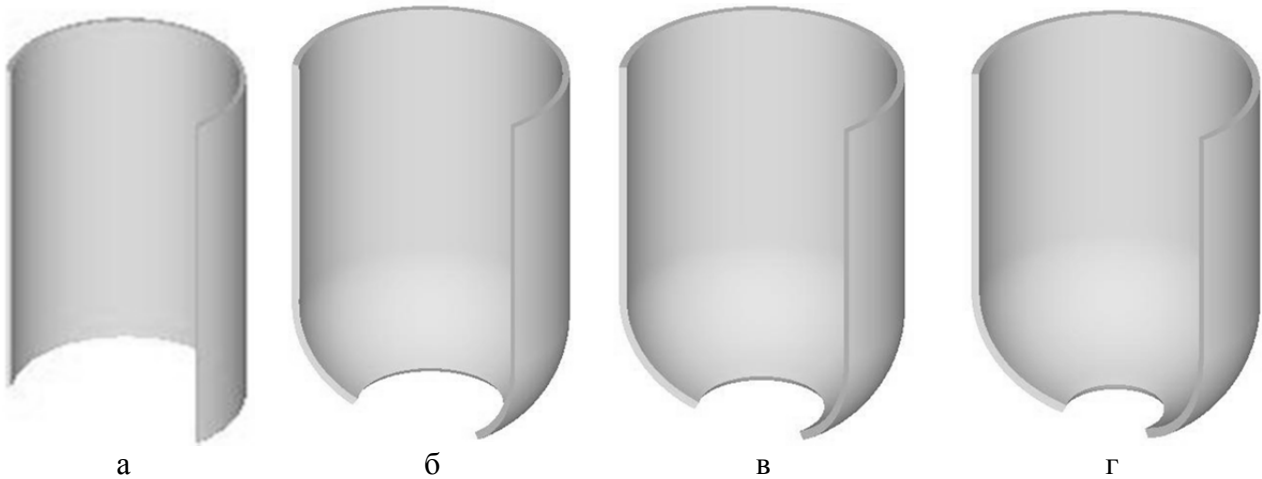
Вихідна заготовка в розрізі (а) та здеформовані заготовки з протитиском $q = 0$ (б), $q = 70$ МПа (в) і $q = 120$ МПа (г)
